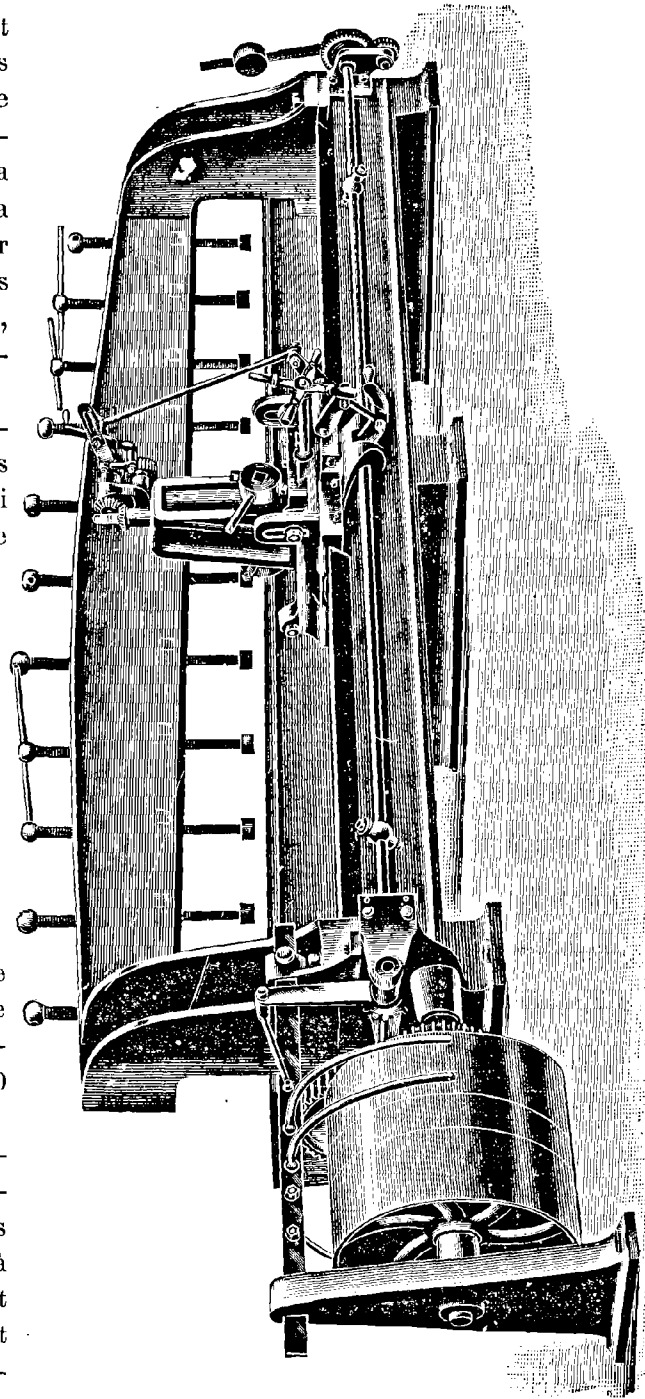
Machine à chanfreiner les tôles de M. Lucas.
